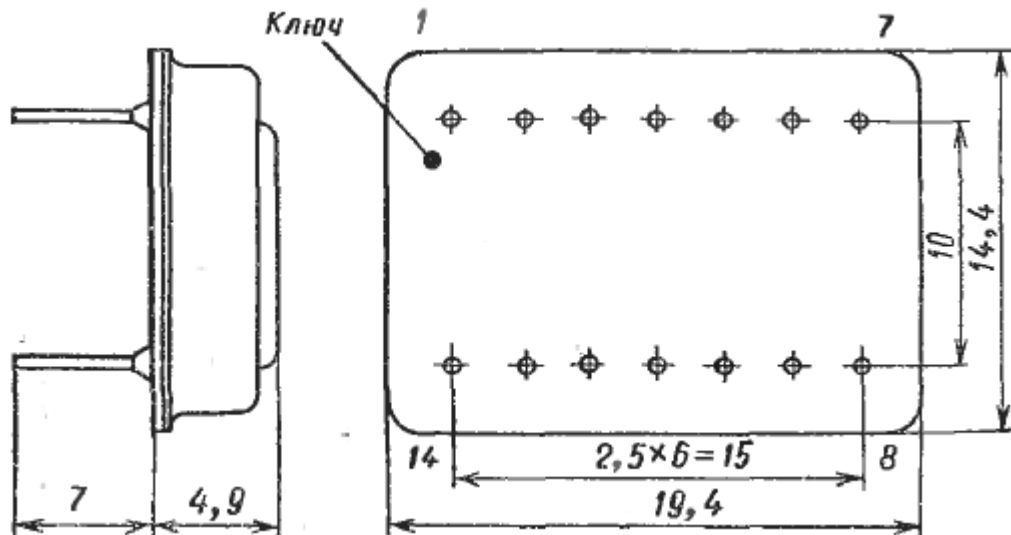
Корпус мікросхеми К295КТ1
